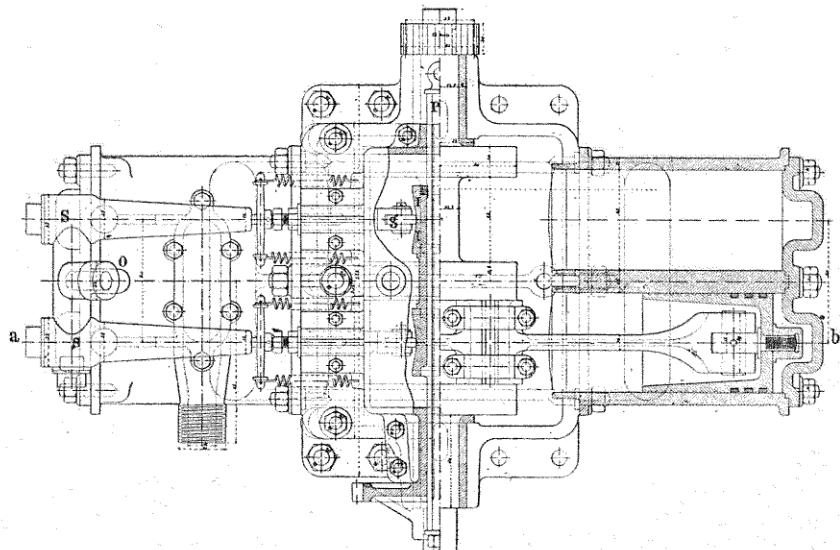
bis. — Moteur Serpollet, plan et 1/2 coupe verticale.
